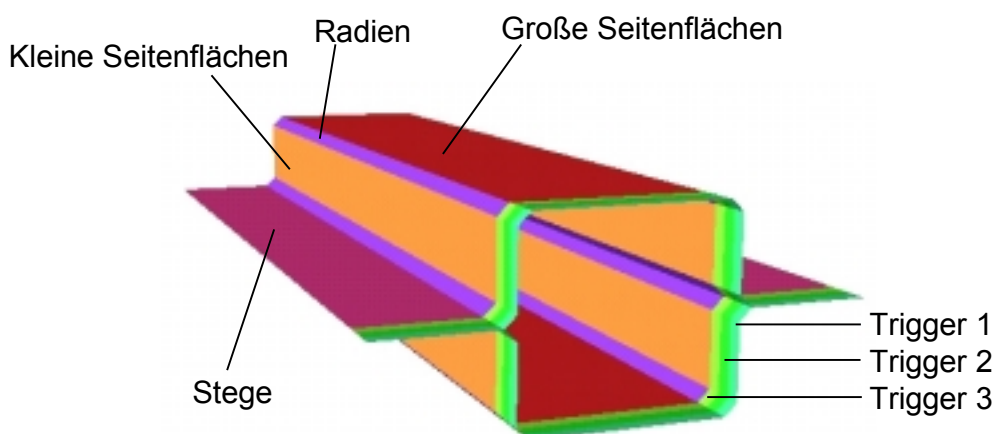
Finite-Elemente-Modell – Rechteckrohr mit Flansch
